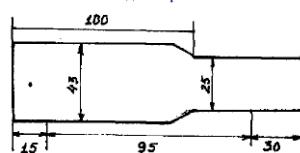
Шаблон для изготовления боковых планок магазинной рамки
